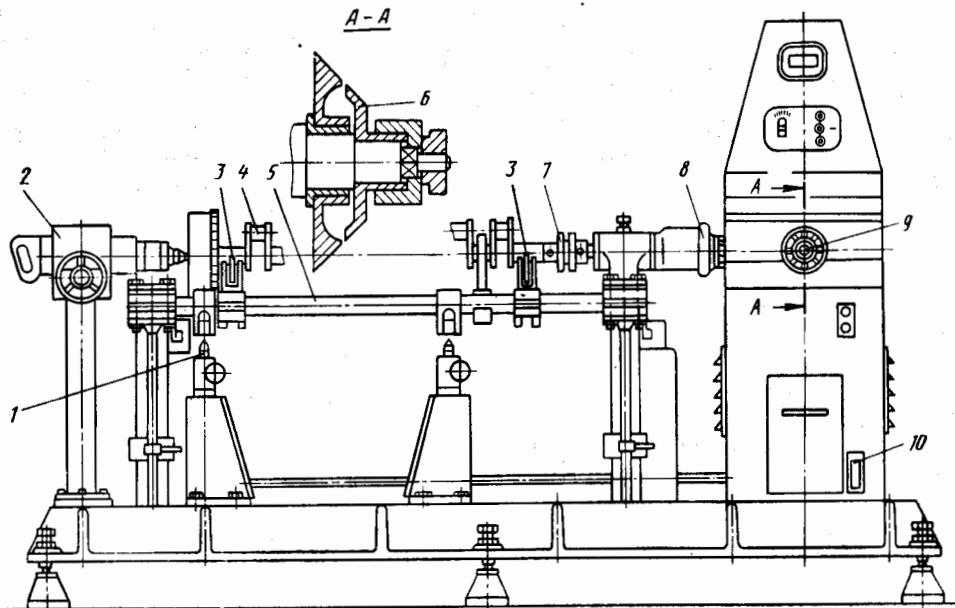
Станок для динамической балансировки коленчатого вала в сборе с маховиком и сцеплением:
